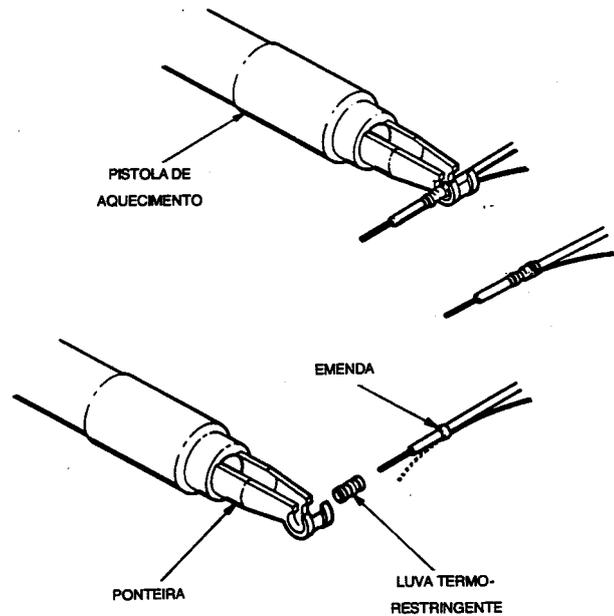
Ferramentas para instalação de luvas termo-restringentes
